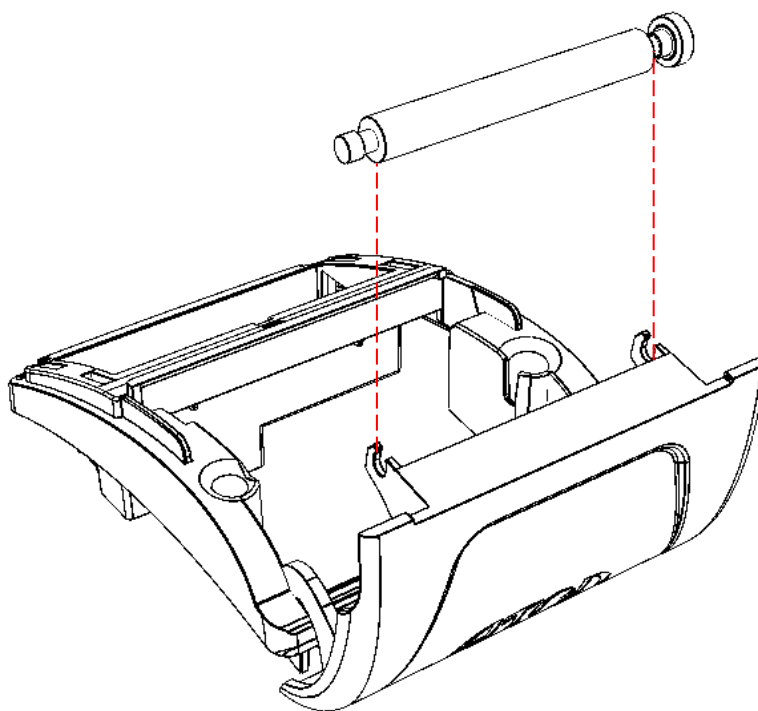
Извлечение прижимного валика из фиксаторов крышки лотка для ЧЛ
